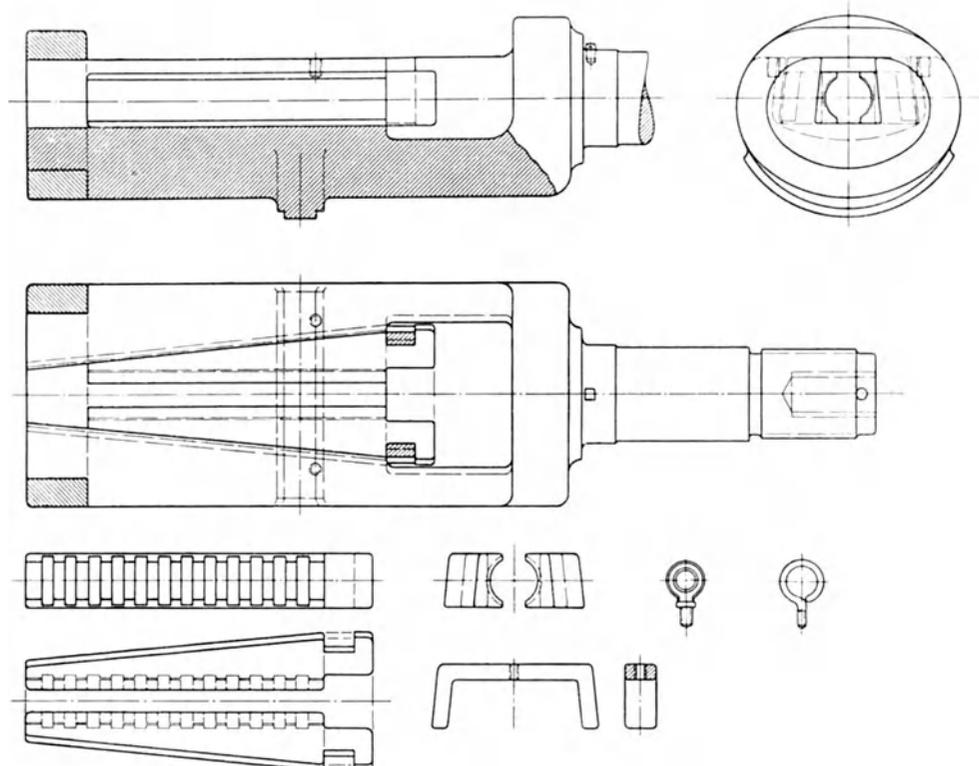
Einspannung für Drahtseile von Martens. Maschinenbaugesellschaft Nürnberg.
